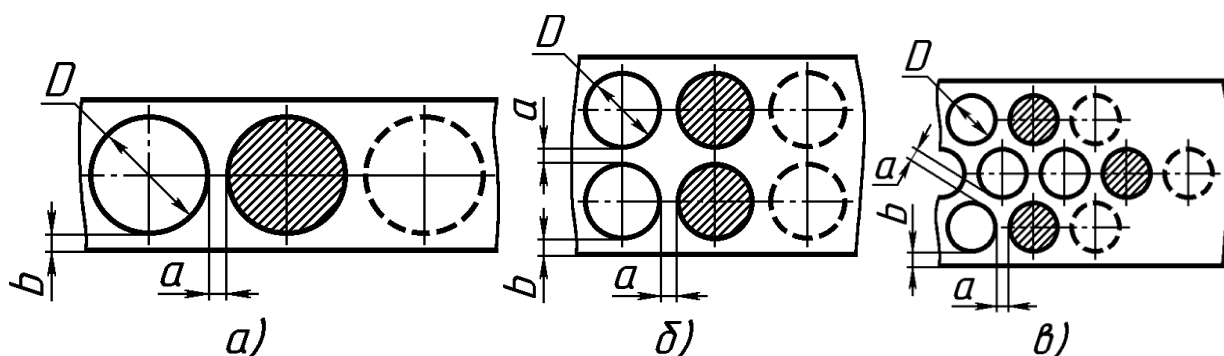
Способы раскроя круглых заготовок: а – однорядный; б – многорядный параллельный и в – многорядный шахматный
